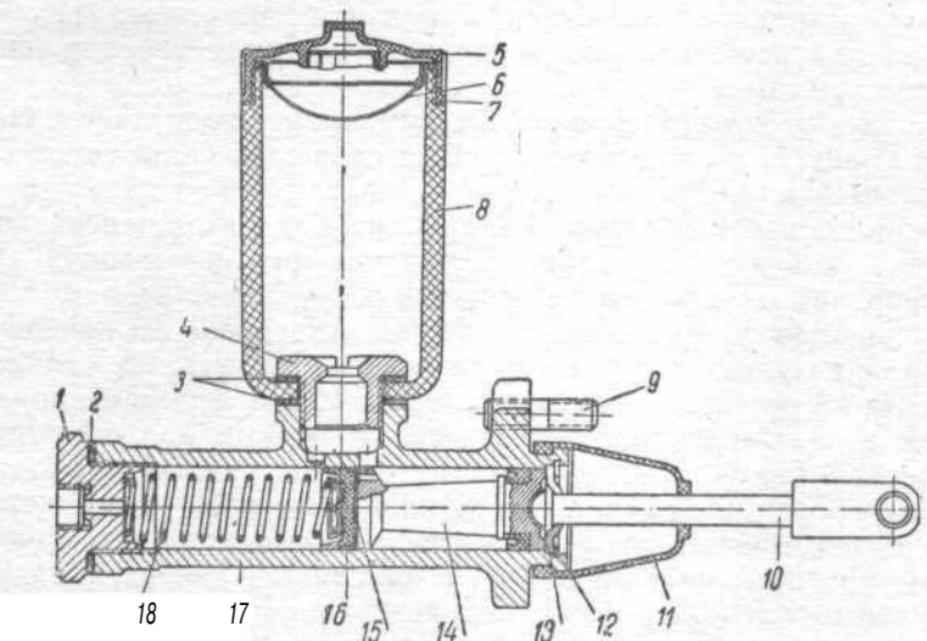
Главный цилиндр гидропривода выключения сцепления:
